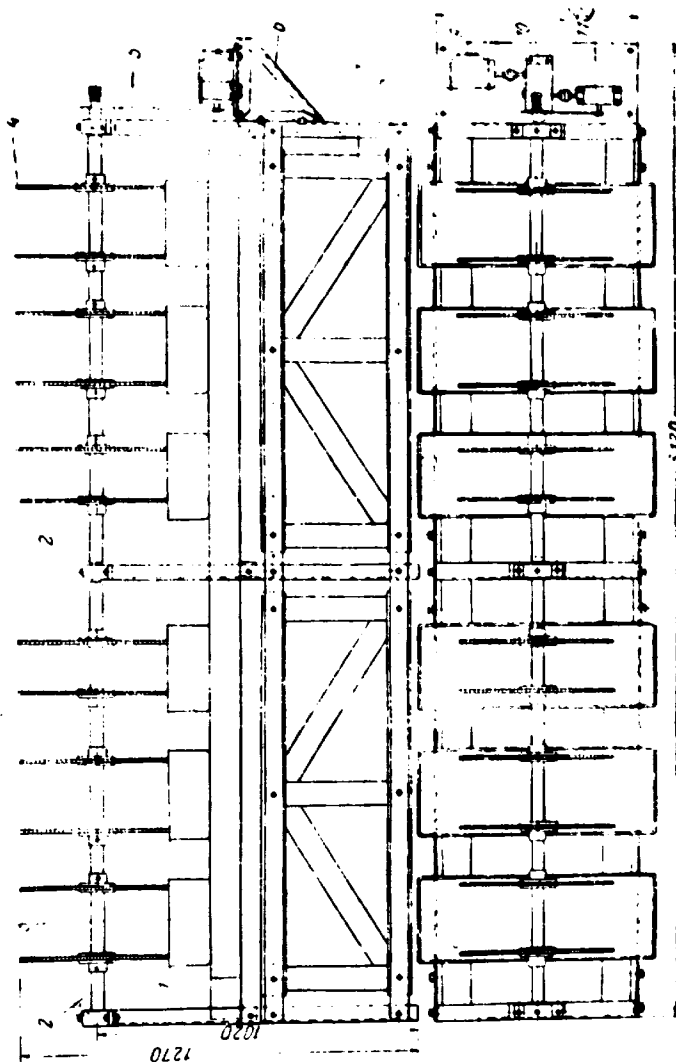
Коррозионное колесо: I - подставка для ванн; 2 - вал; 3 - ванна; 4 - диск; 5 - цепь; 6 - столик; 7 - рама; 8 - станина; 9 - электромотор; 10 - редуктор  $i = 1:25$ ; II - редуктор  $i = 1:1660$ .
